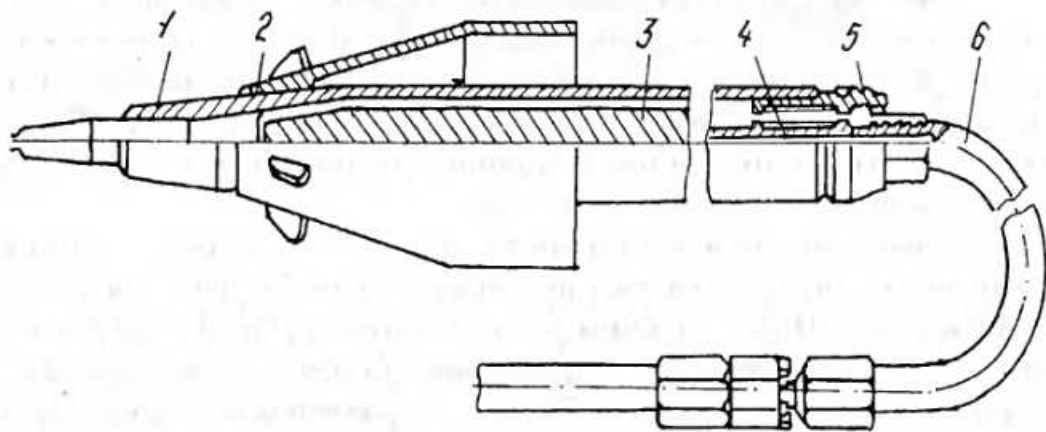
Пневмопробивач: 1-корпус, 2-знімний розширювач, 3-ударник, 4-золотник, 5-реверсивний пристрій, 6-рукав
